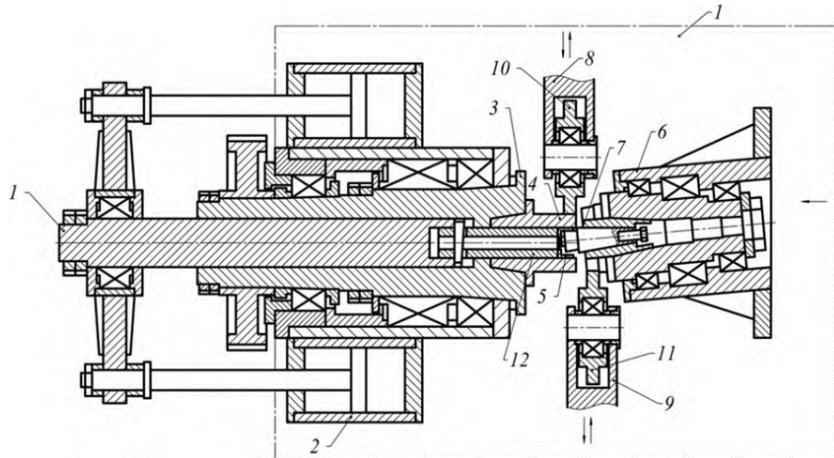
Обкочувальний інструментальний блок з конічним валком для виготовлення заготовок методом ШО: 1 – шток силового навантаження поздовжньої подачі заготовки; 2 – гідроциліндр; 3 – оправка обертального приводу матричного блоку; 4 – матриця; 5 – заготовка; 6 – блок валковий; 7 – валок конічний; 8, 10 – блок циліндричного валка радіального підпору матриці (заготовки); 9, 11 – блок циліндричного валка радіального підпору конічного валка; 12 – штовхач.
